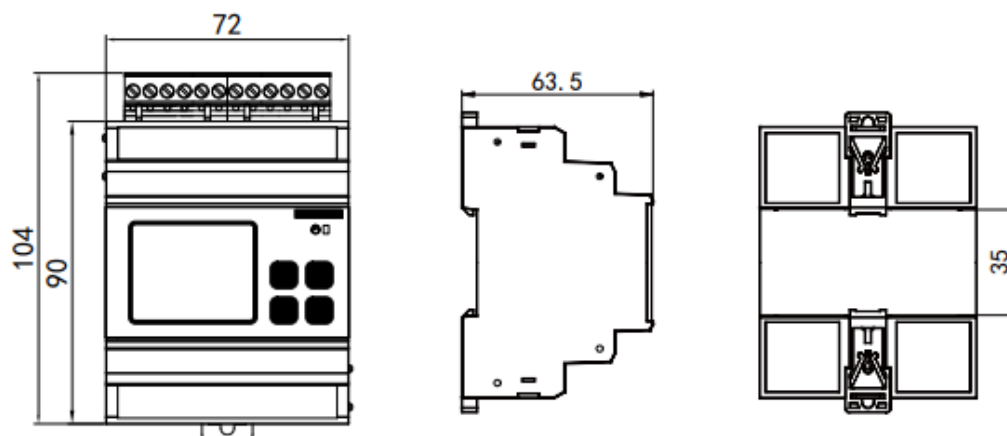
Внешний вид и габаритные размеры модуля измерительного КСМ-М1-1 и КСМ-М1-2
